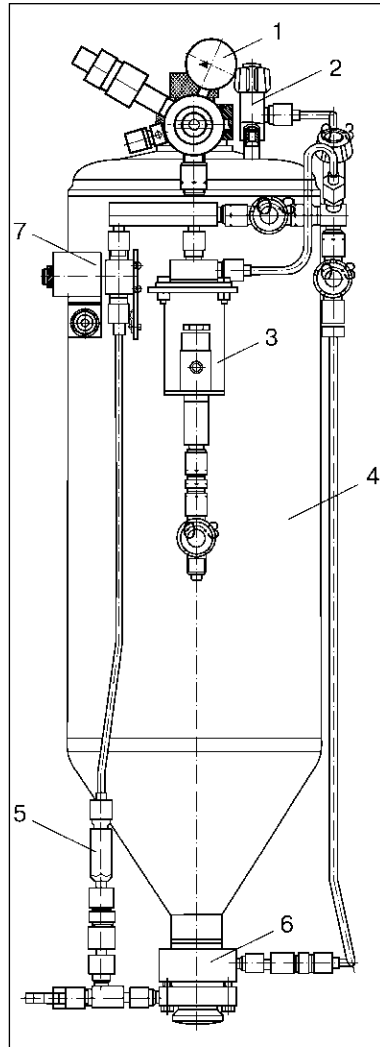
Флюсопитатель: 1 — редуктор; 2 — вентиль для сброса давления; 3 — пневмораспределитель; 4 — бачок для флюса; 5 — обратный клапан; 6 — циклон; 7 — электромагнитный клапан
